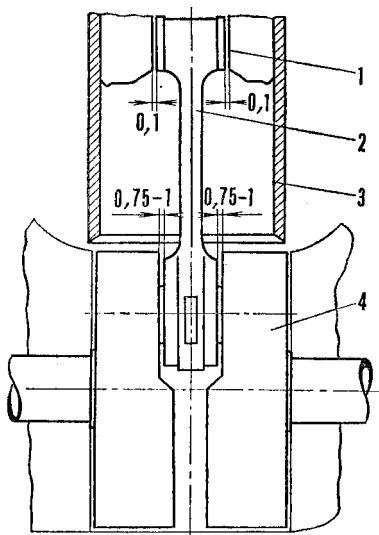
Центровка шатуна: 1 — стальные шайбы; 2 — шатун; 3 — поршень; 4 — коленчатый вал
